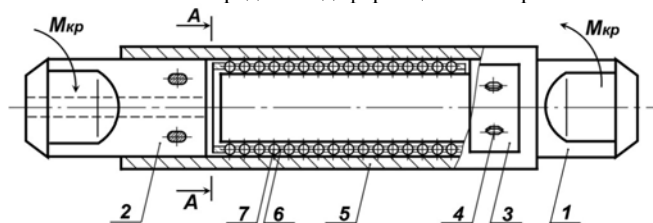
Устройство для испытания трубчатых образцов на пластичность:
